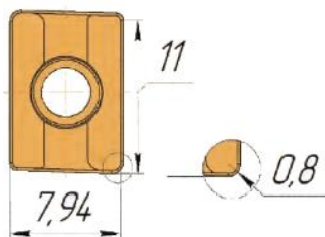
Размеры режущей пластины (ZPNT 1506..R)
